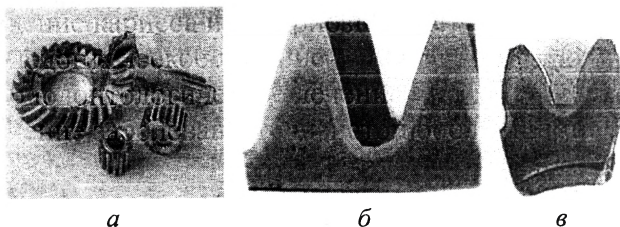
Закалка ОПЗ шестерен МАЗ из сталей пониженной прокаливаемости: а — шестерни, подверженные закалке; б — зоне закалки на ведомой шестерне главной пары; в — зона закалки на шестерне колесной передачи
